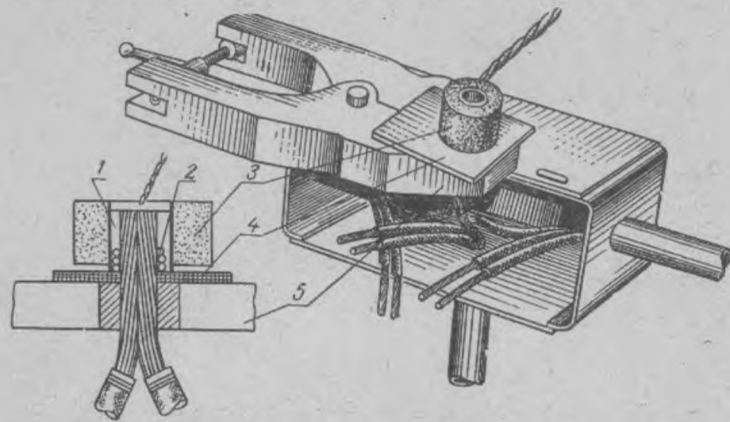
Термитная сварка алюминиевых жил большого сечения
